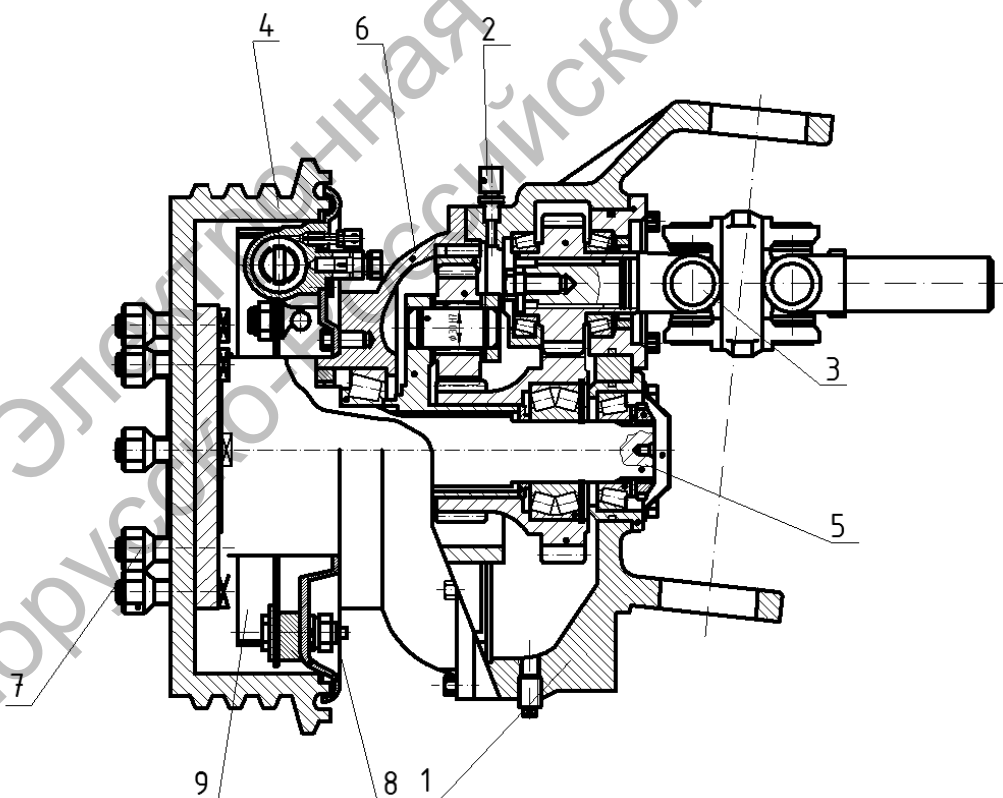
Основные элементы тормозного механизма передних ведущих колес трактора с неподвижными опорами: 1 – корпус редуктора; 2 – сапун; 3 – карданная передача; 4 – гидроцилиндр; 5 – полуось; 6 – крышка редуктора; 7 – болт; 8 – эксцентрик; 9 – колодка тормозная
